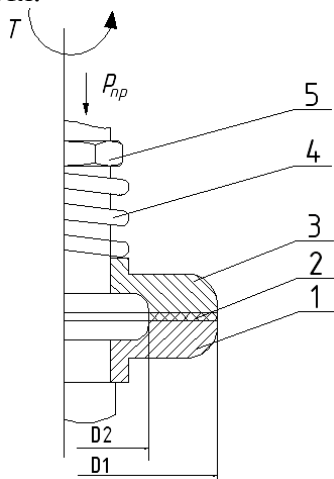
Схема фрикційного однодискового запобіжного механізму: 1–нерухома частина механізму; 2–фрикційна накладка; 3–рухома частина механізму; 4–притисна пружина; 5–регулююча гайка
